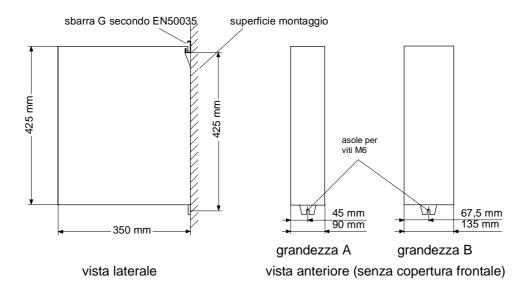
Disegni d'ingombro per montaggio grandezze A, B
